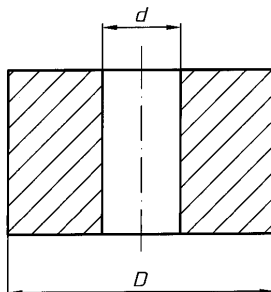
Обозначения размеров заготовки и обрабатываемого отверстия
